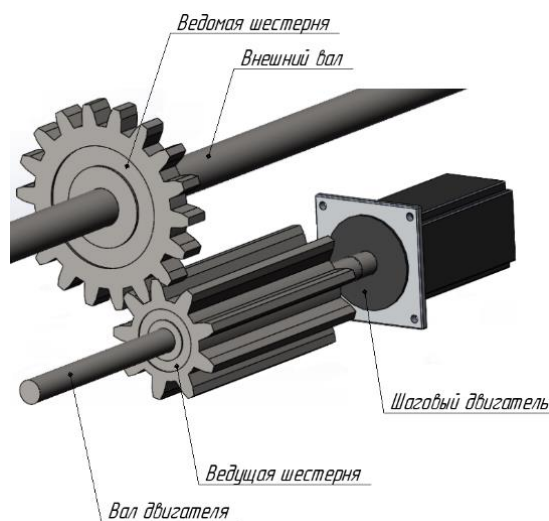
Общий вид механизма для передачи вращательного движения
